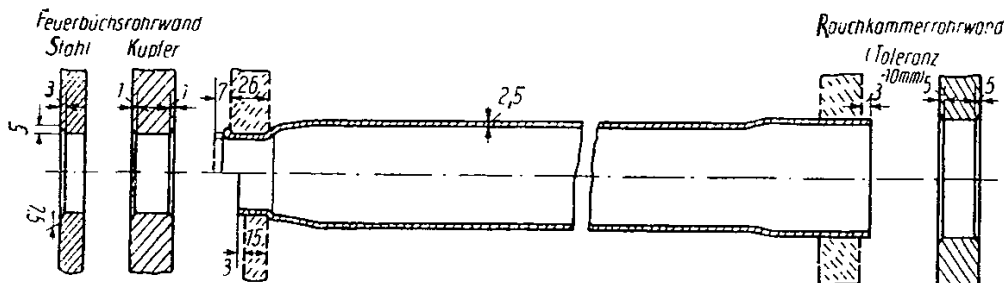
Festeingewalztes und gebördeltes bzw. geschweißtes Heizrohr
